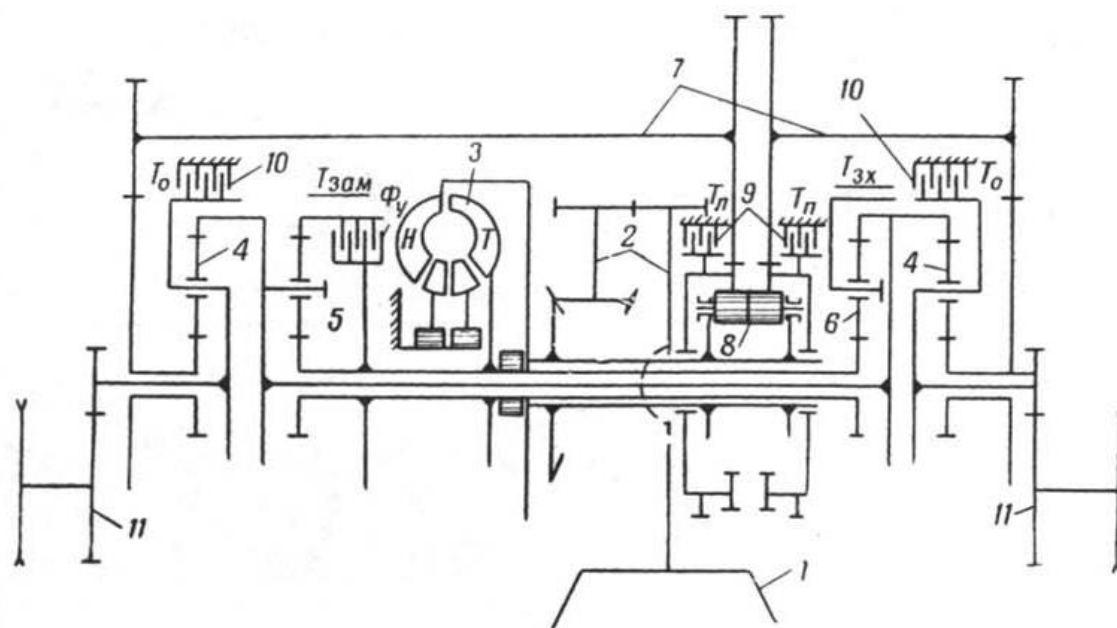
Принципиальная кинематическая схема гидромеханической трансмиссии «кросс-драйв»: 1 – двигатель; 2 – первичный редуктор; 3 – комплексный гидротрансформатор; 4 – суммирующие планетарные ряды; 5 – планетарный ряд замедленной передачи; 6 – планетарный ряд заднего хода; 7 – дополнительные передачи; 8 – простой цилиндрический дифференциал; 9 – тормоза поворота; 10 – остановочные тормоза; 11 – бортовые передачи.
